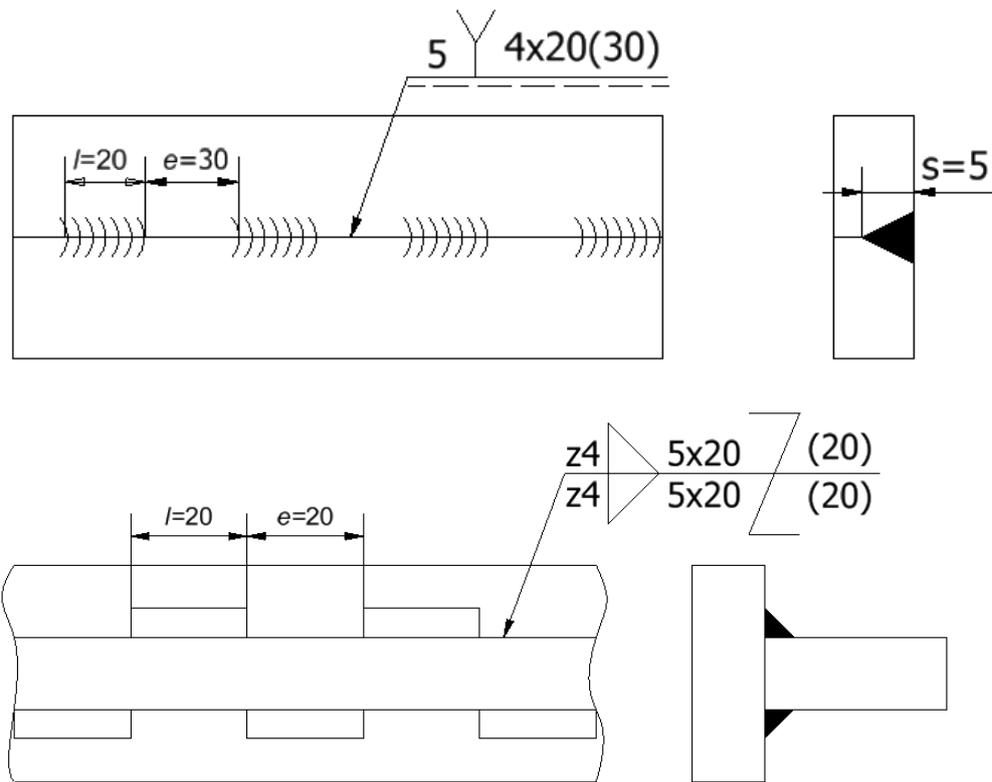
Dimensionamiento de uniones soldadas: a) Soldadura a tope, b) doble soldadura en ángulo intermitente alternada.
